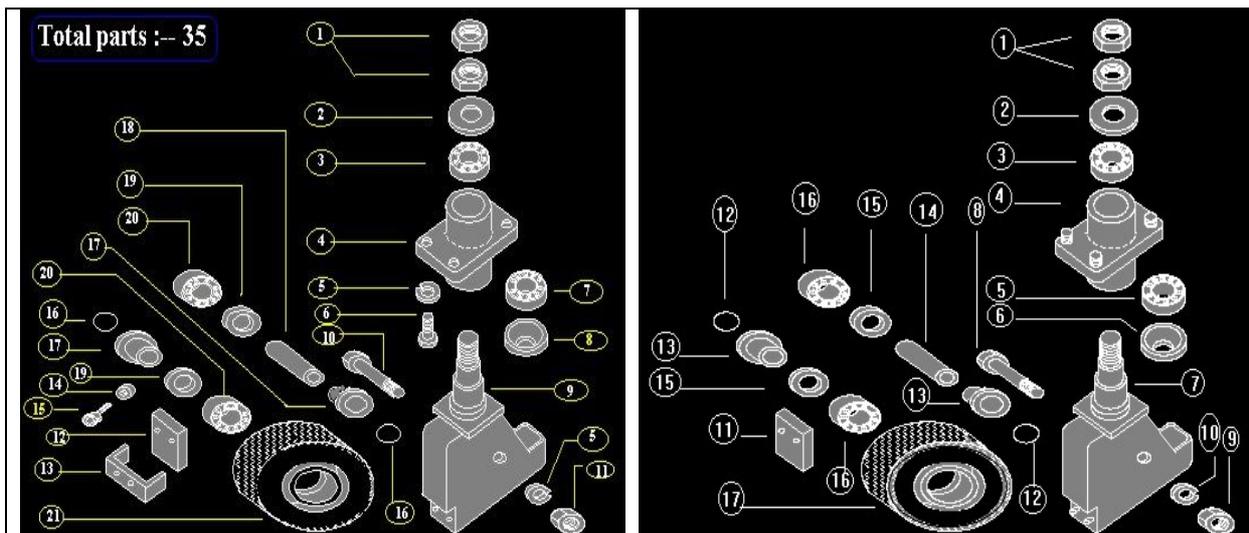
Внешний вид исходной и усовершенствованной конструкции сборочной единицы
